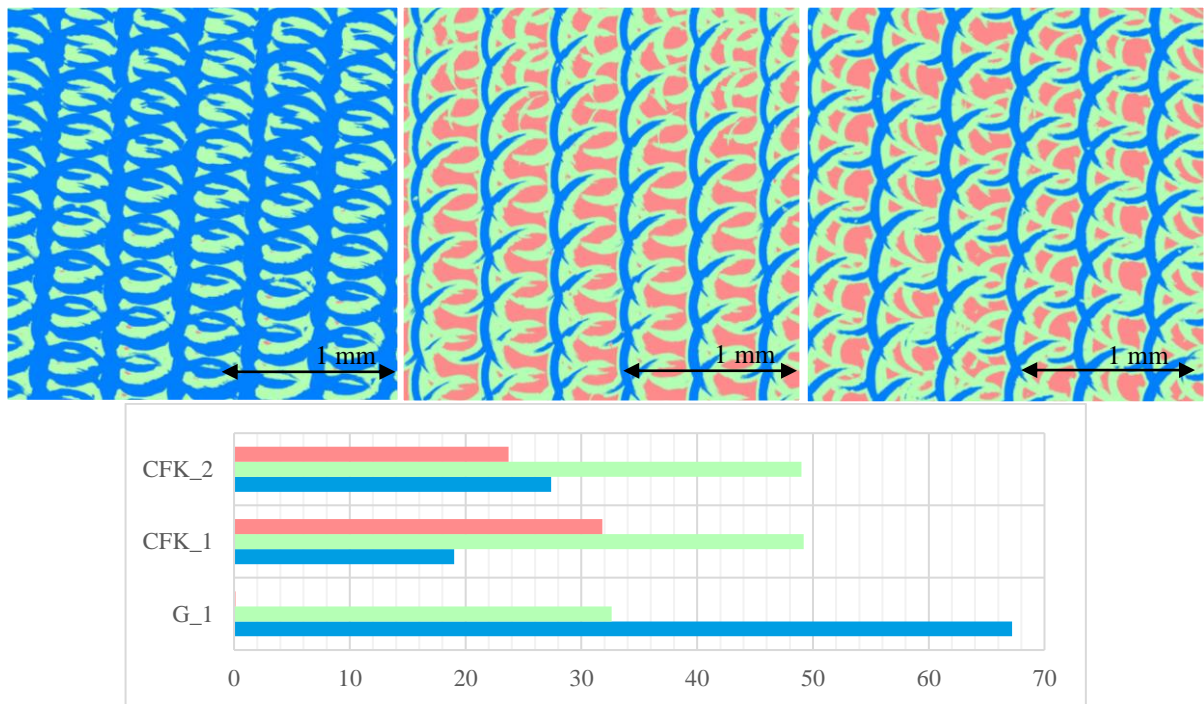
Hörenschnitt der Fläche der gefrästen Bauteile; links: Gussachse (G_1) ; Mitte: CFK-Achse (CFK_1); rechts: CFK-Achse (CFK_2)
